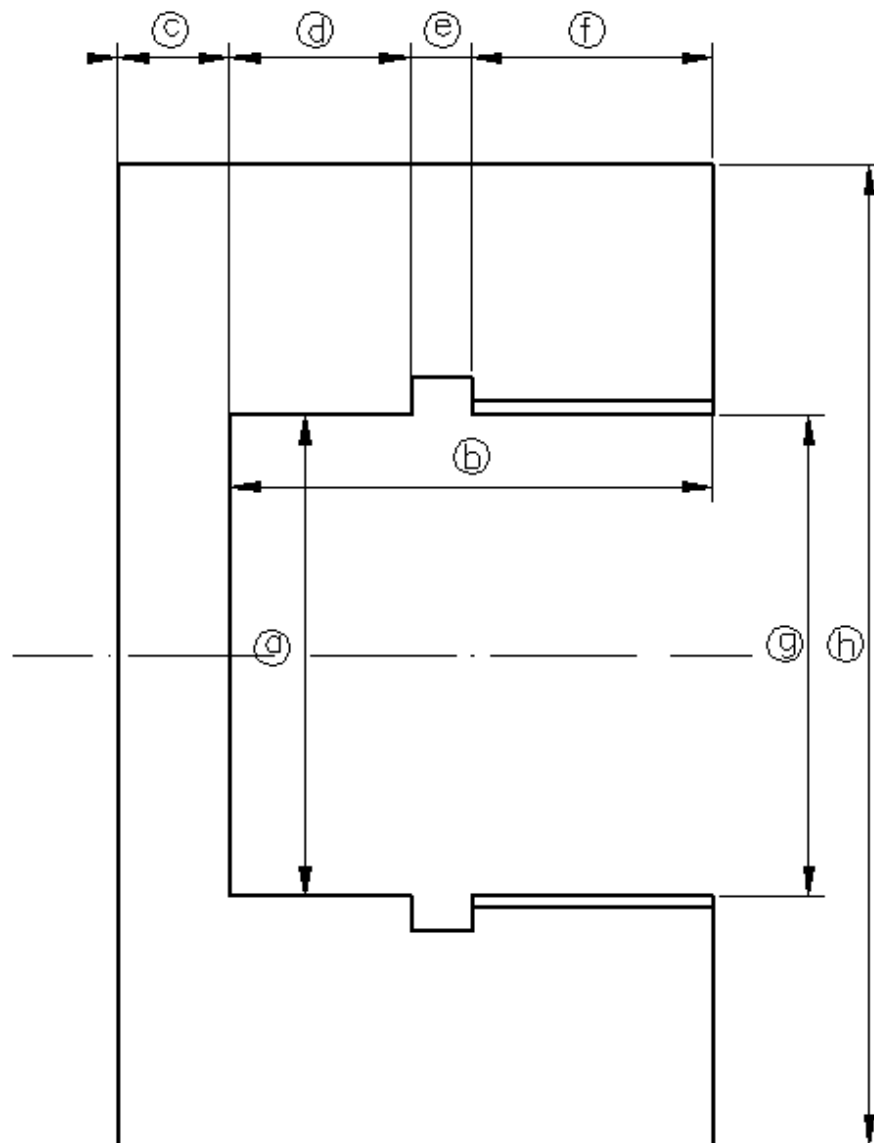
Plano guía comprobar dimensiones para la prueba #2
